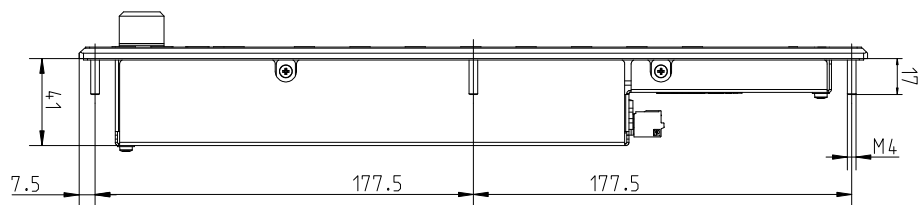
Abmessungen: Frontplatte der VDP 40.3BI-Geräte
